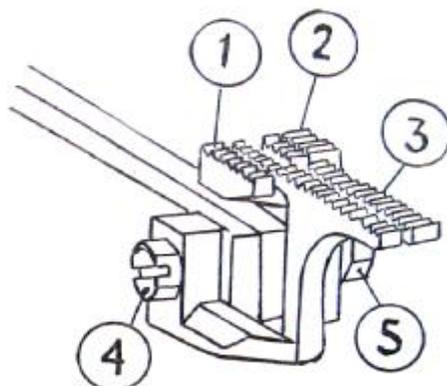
Регулировка положения зубцов реек по высоте
